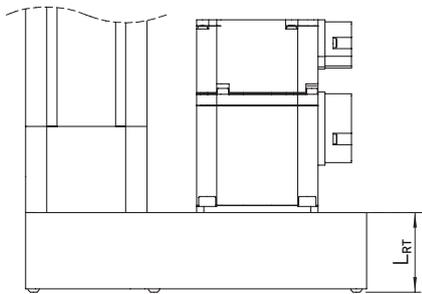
Motoranbindung Linearmodule HM-S mit Riementrieb
